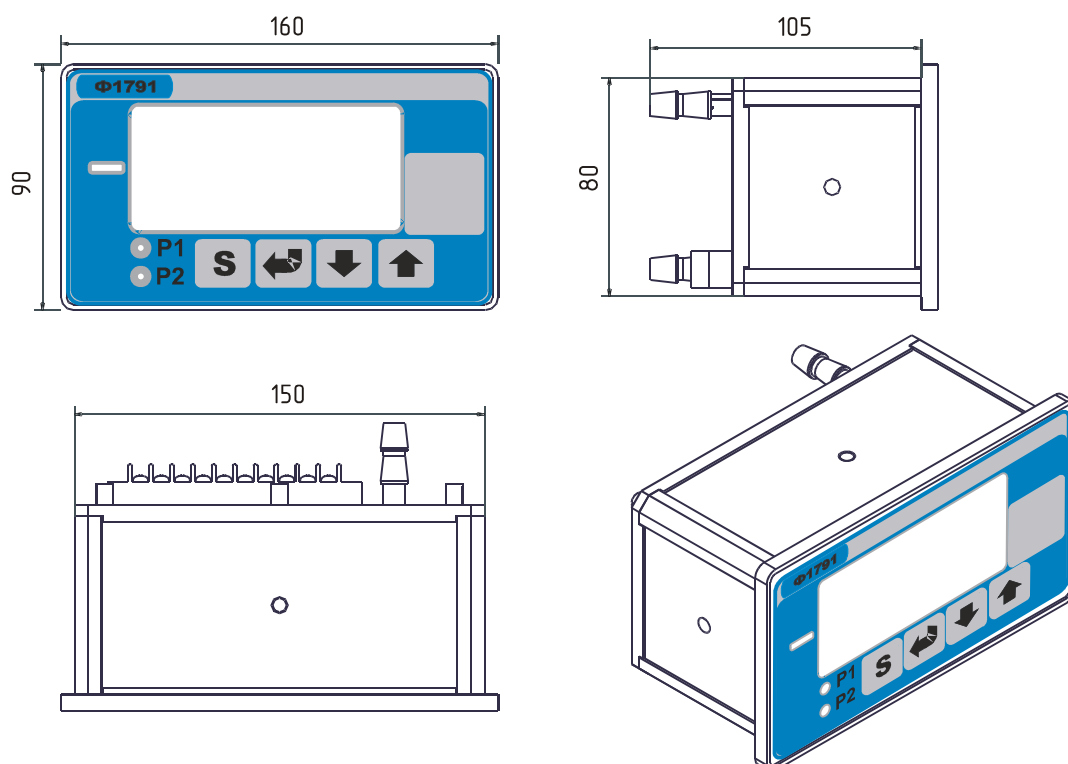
Внешний вид и габаритные размеры Ф1791.1
